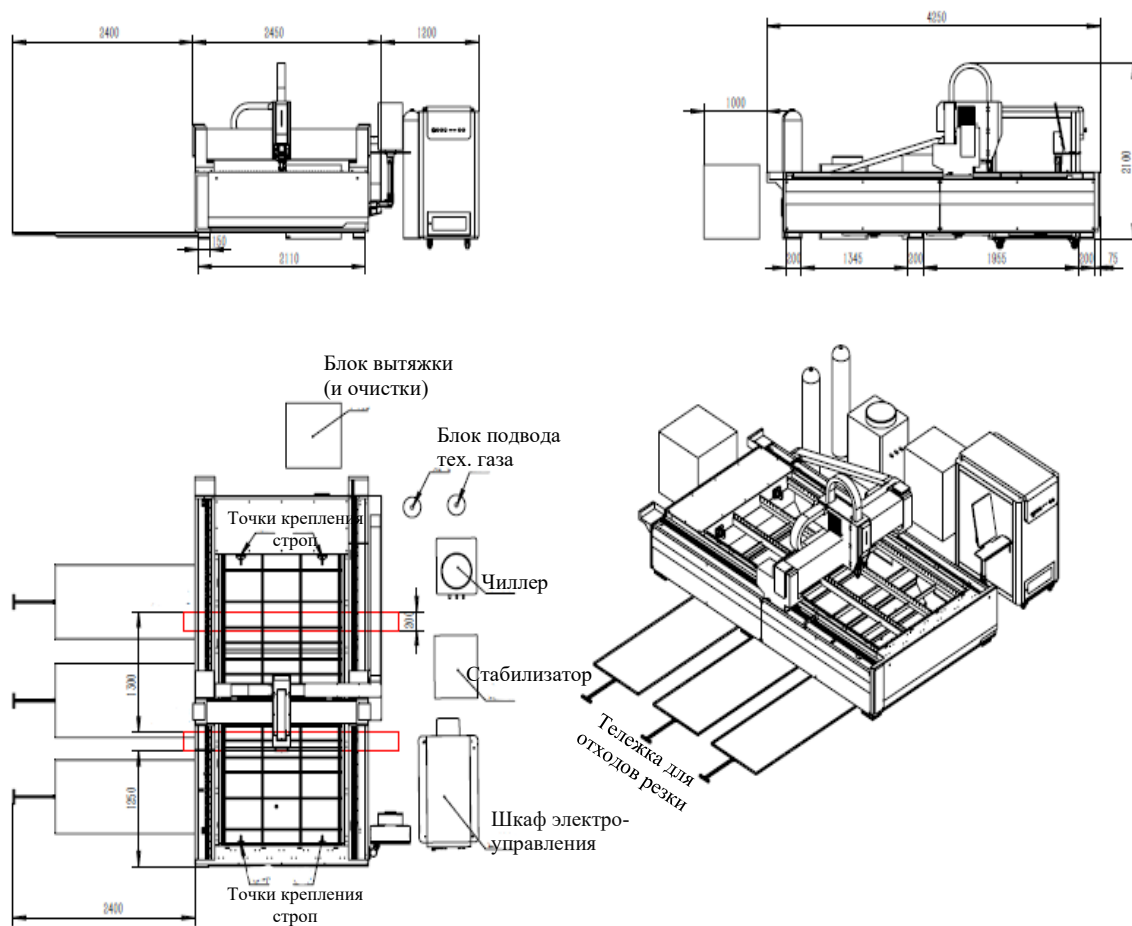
Схема размещения MetalTec 1530B (6000W)
